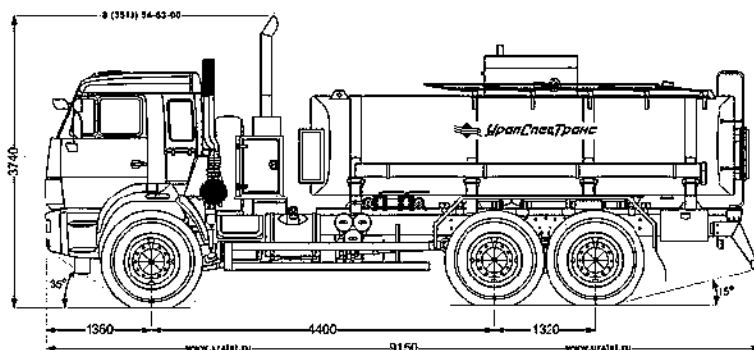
Габаритні розміри паливозаправника АТЗ-12-43118
